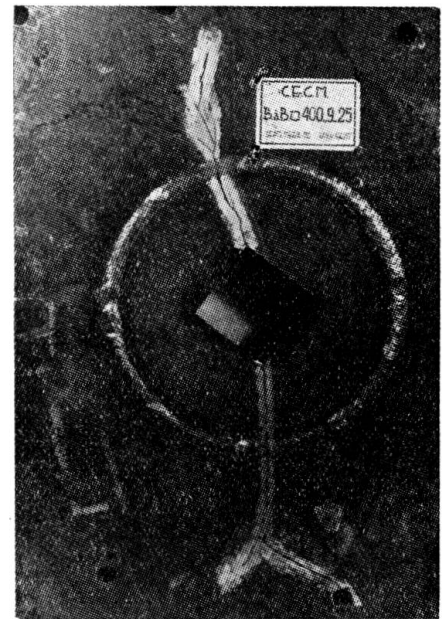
Rupture après refroidissement d'un disque contenant une ouverture à angles vifs réalisée avant soudage
